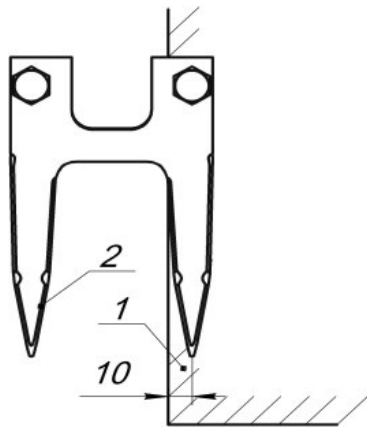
Схема центрирования ножа: 1 – боковина; 2 – палец;
